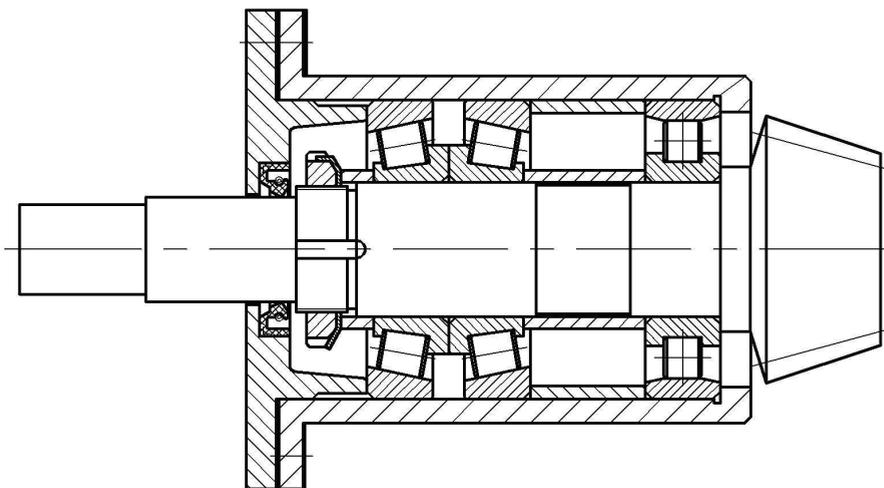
Установка вала-шестерни с фиксирующей и плавающей опорами
